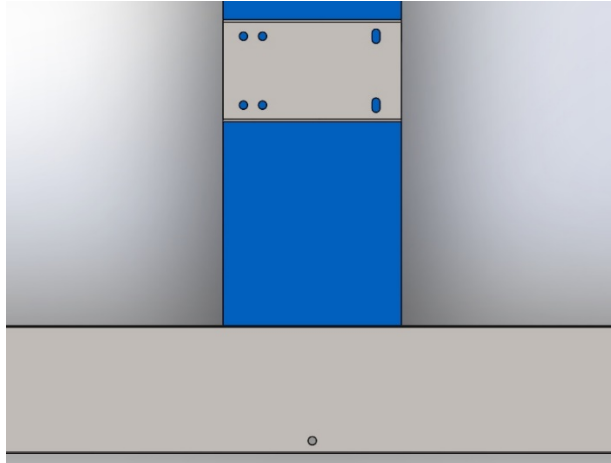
Detalle de taladros para unidades de rodamiento y conjunto de medición
